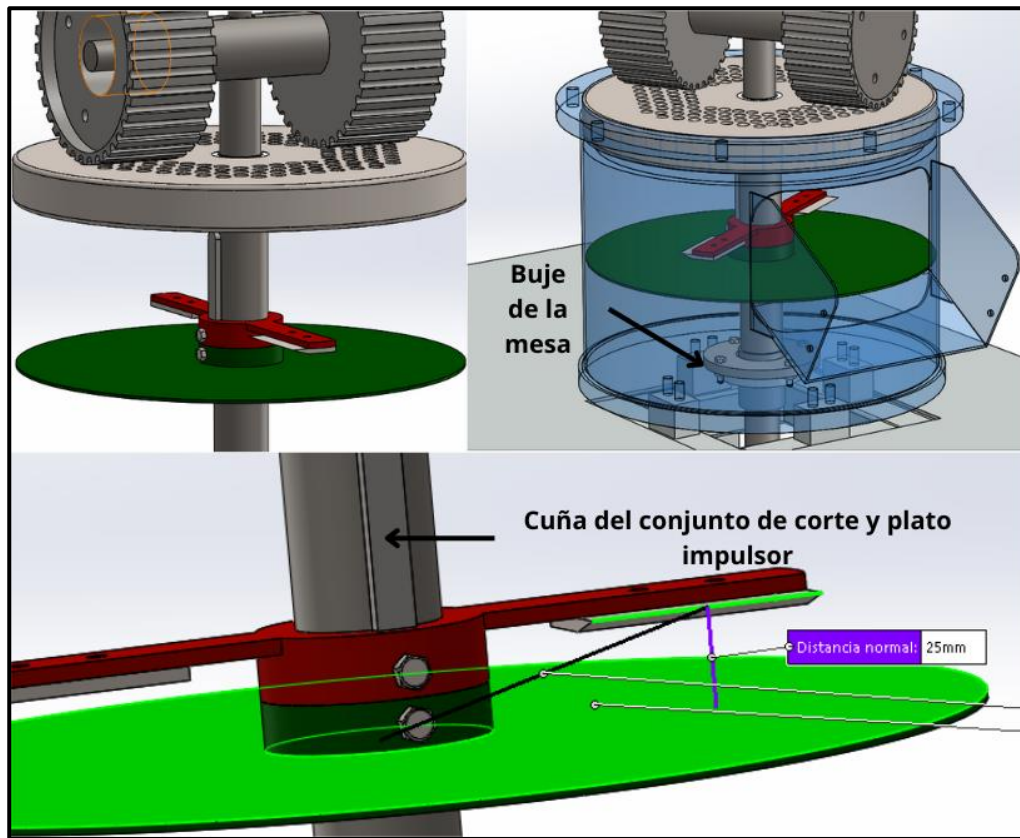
Posición del Conjunto de Corte y Plato impulsor.
